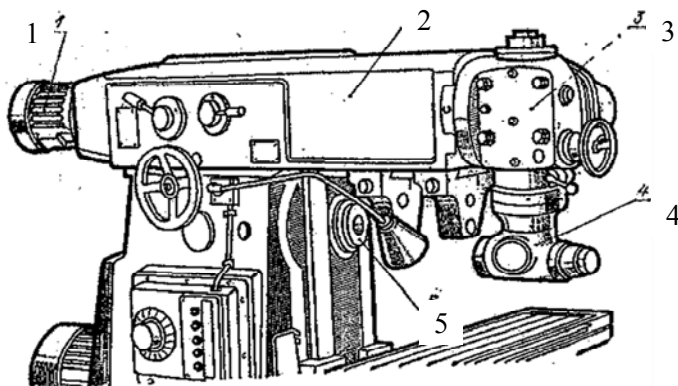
Общий вид широкоуниверсального консольно-фрезерного станка модели 6P82M
